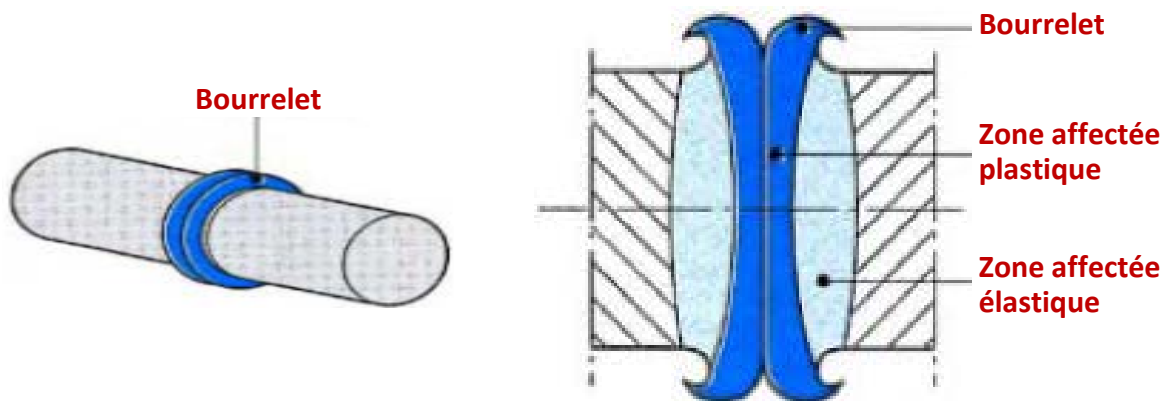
Vue globale et en coupe d'un joint soudé par friction [14]
